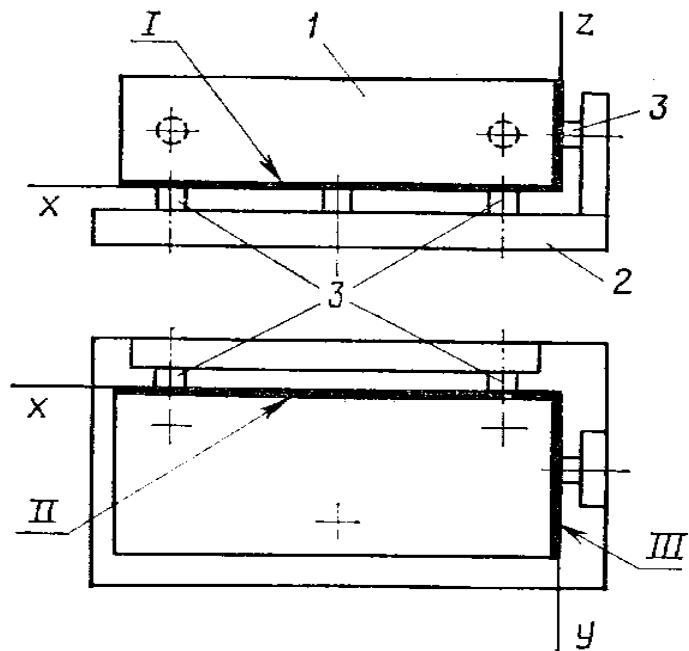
Схема базирования призматической заготовки в приспособлении:
